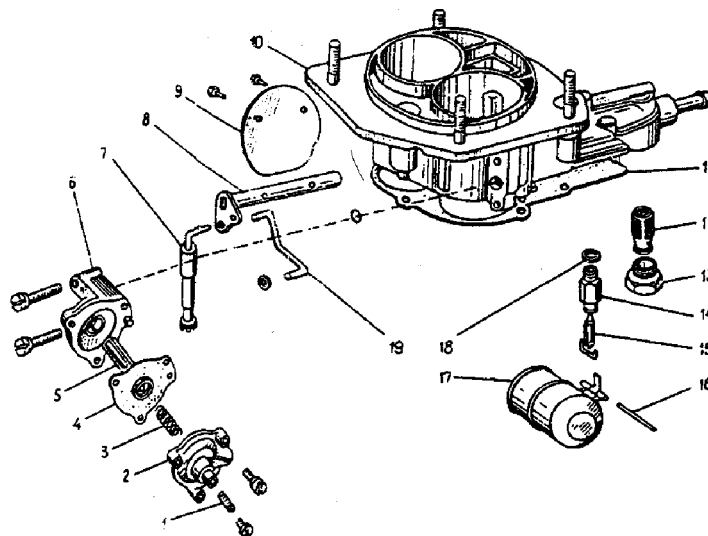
Componentes da tampa do carburador: 1 - parafuso de ajuste; 2 - tampa do dispositivo de partida; 3 - mola; 4 - diafragma; 5 - haste do diafragma; 6 - corpo do dispositivo de partida; 7 - haste telescópica; 8 - eixo da borboleta do afogador; 9 - borboleta do afogador; 10 - tampa do carburador; 11 - junta; 12 - filtro; 13 - tampa do filtro; 14 - assento da válvula de agulha; 15 - válvula de agulha; 16 - eixo da bóia; 17 - bóia; 18 - junta; 19 - haste do dispositivo de partida.
